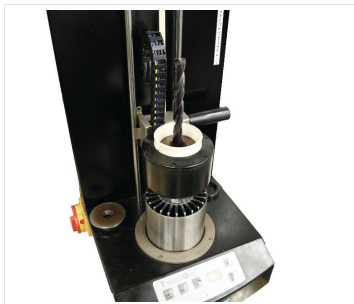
Schrumpffutter mit Werkzeug erwärmen
